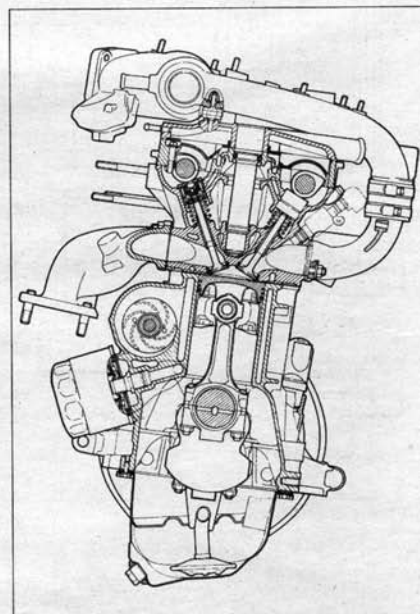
Поперечный разрез двигателя ВА3–2112
